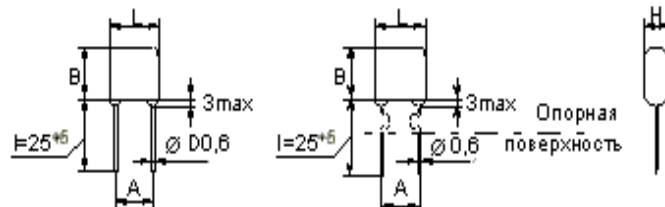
Габаритні розміри конденсатора типу К10-176
